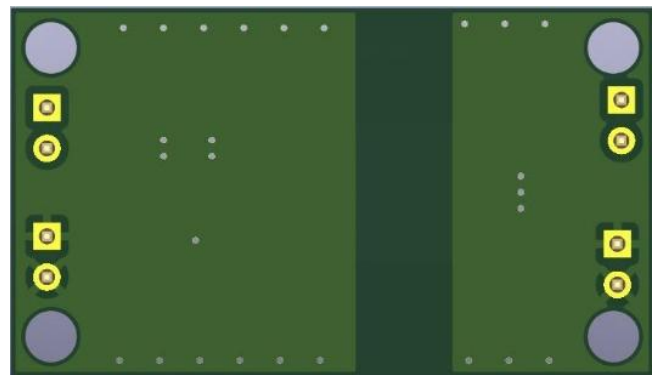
PCB 版图反面 (尺寸: 23x 40mm)
